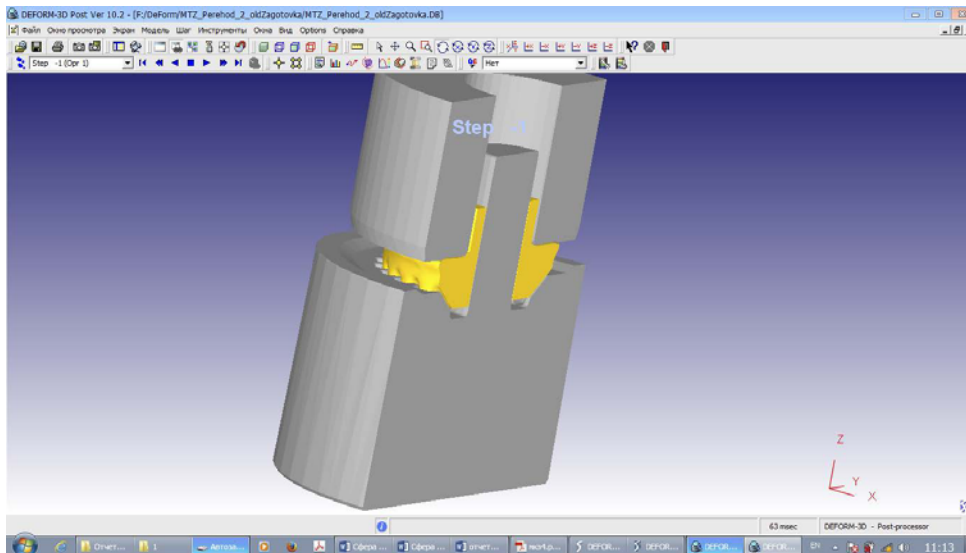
3D-модель инструмента и заготовки для второго перехода штамповки конического зубчатого колеса
